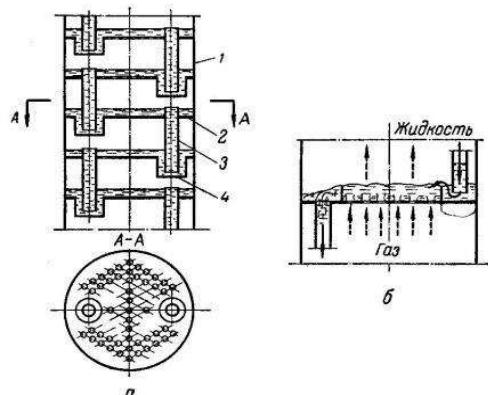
Ситчатая колонна: а - схема устройства колонны; б - схема работы тарелки; 1 – корпус; 2 – тарелка; 3 – переливная труба; 4 – стакан.
